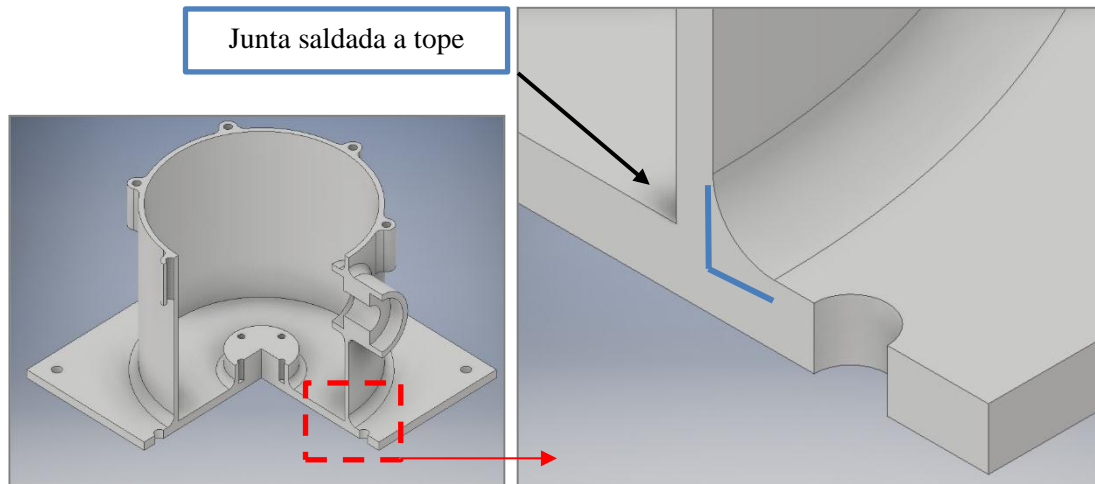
Diseño de la junta soldada para la cámara de engranajes. Elaborado por.: Fernando Albán & Ángel Arias
